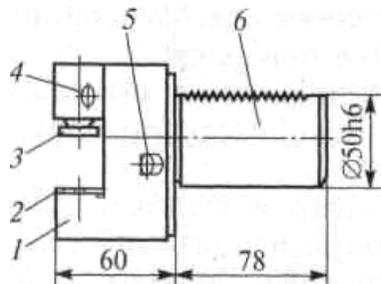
Резцовый блок с цилиндрическим хвостовиком.
